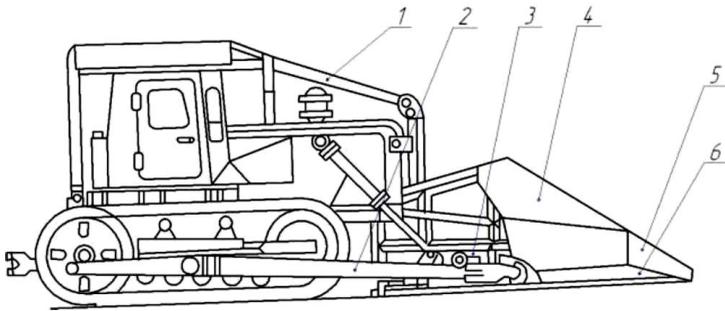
Кущоріз ДП-24: 1– огорожа; 2 – рама; 3 –головка знімна; 4 – відвал; 5 - клин-колун; 6 – ніж
